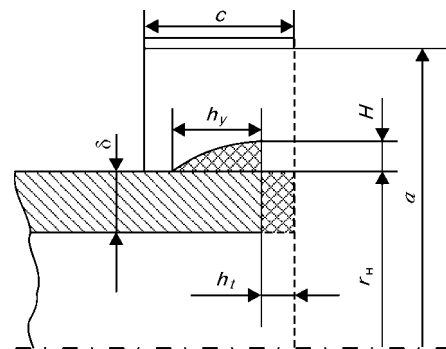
Схема участка осадки кромок при высокочастотной сварке и сваркопайке труб встык
